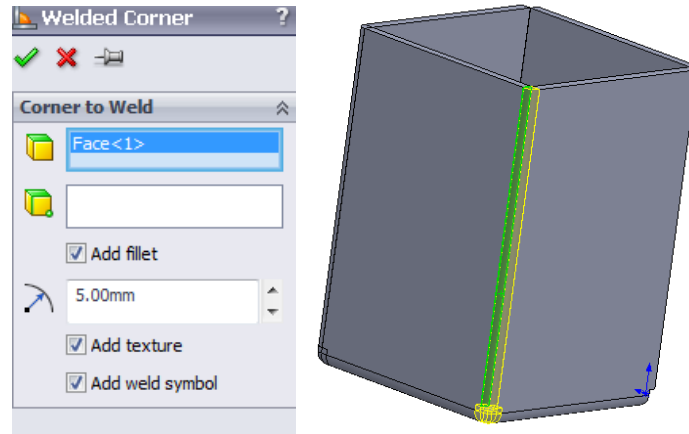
Exemplu de utilizare a opțiunii *Welding Corner
